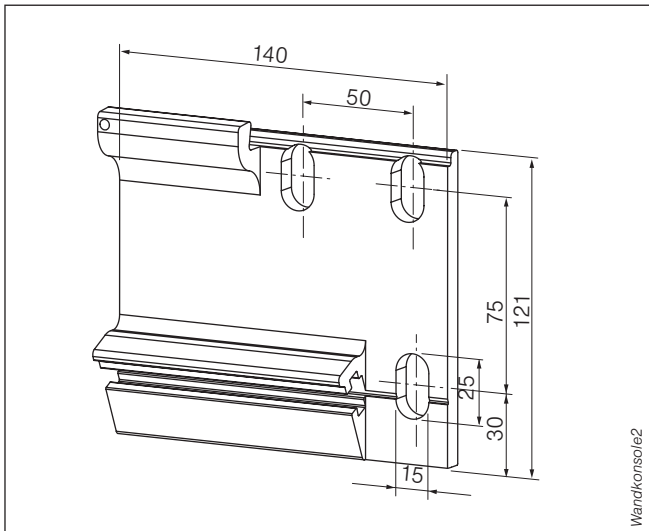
Consola tipo B – Fijación mural con 3 taladros –
